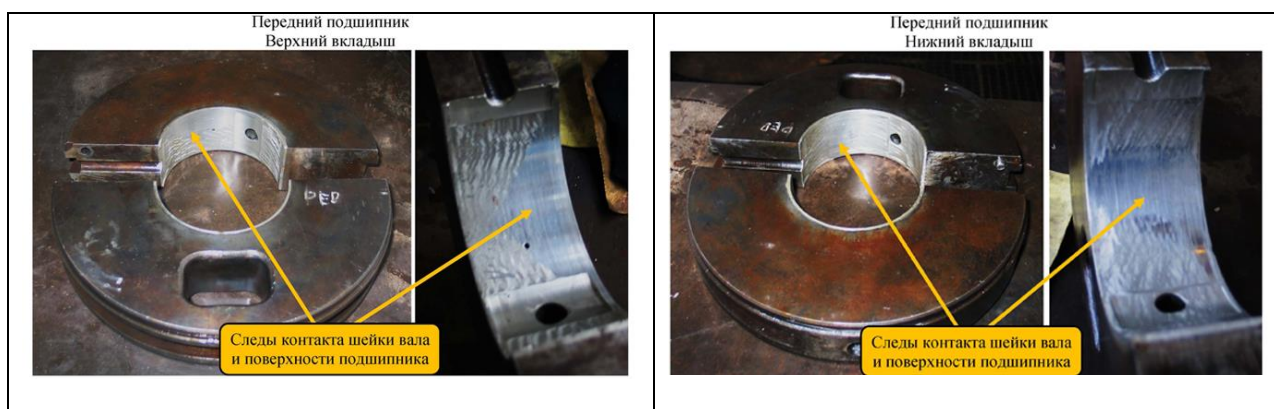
Детали переднего подшипника компрессора: на верхнем и нижнем вкладышах видны следы контакта шейки вала и поверхности подшипника
